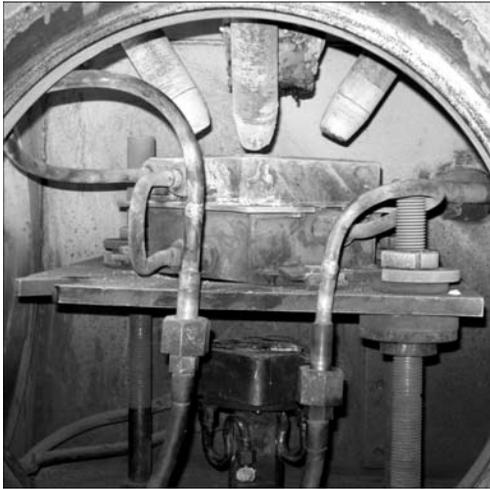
Подготовка установки УПП-3 для плавки расходимой заготовки в проходной кристаллизатор квадратного сечения
